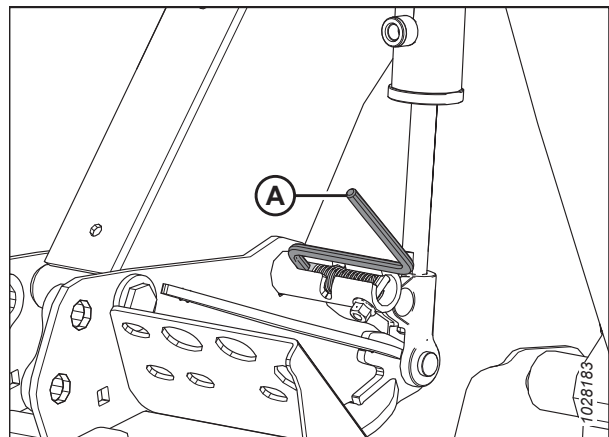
Зафиксированный предохранительный упор мотовила — центральный рычаг
